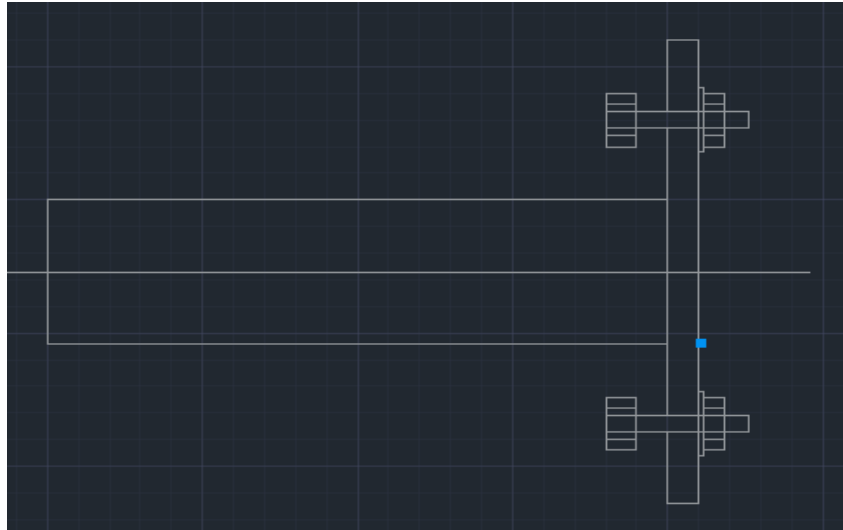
Cálculo de los pernos que soporta la placa del motor de arranque
